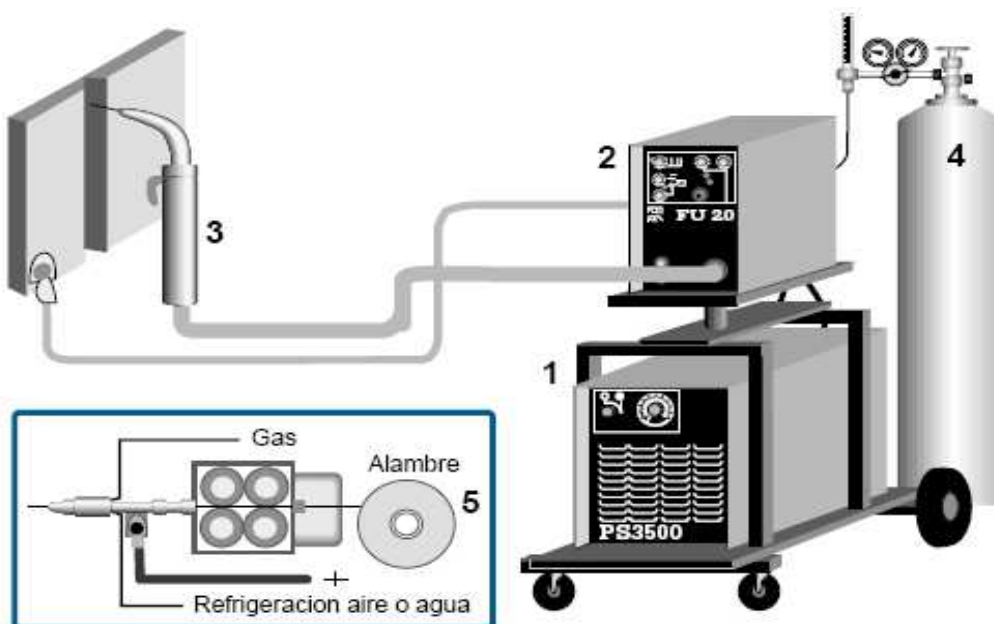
Equipo Para Soldadura GMAW
